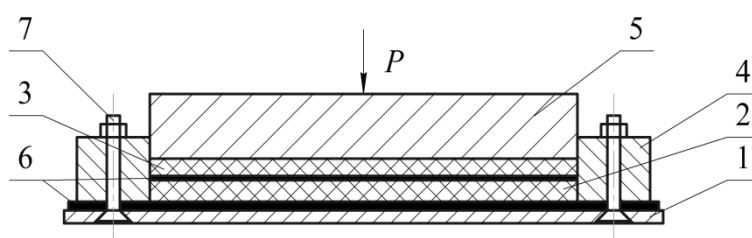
Пресс-форма для изготовления плоской квадратной пластины композита
